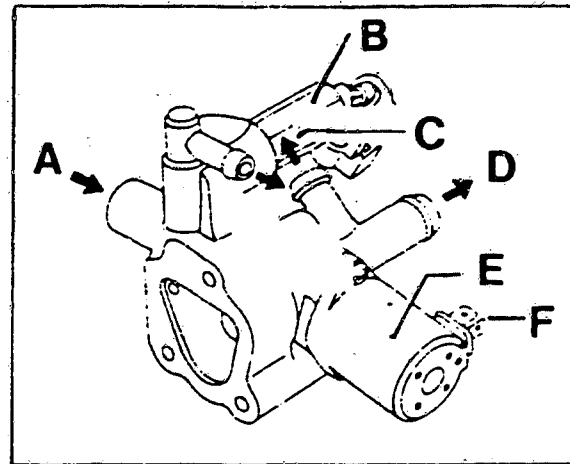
Leerlaufstellung am Zusatzluftsteuerventil. A Leerlaufeinstellschraube – B FICD Magnetventil – C zum Luftregelventil – D zum Luftführungs kanal – E AAC-Ventil – F Verbindungsstecker.
